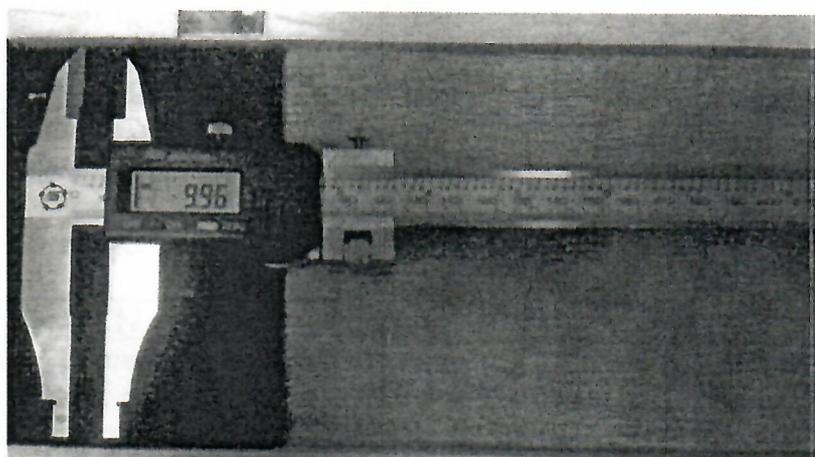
Общий вид штангенциркулей типа IIIЦЦ-II.
